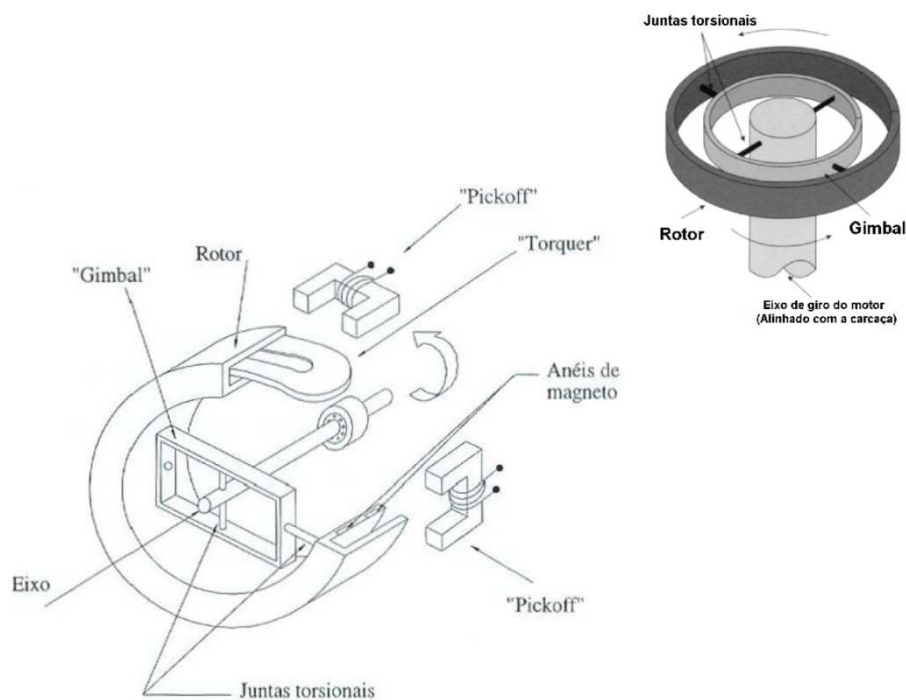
Representações do rotor e do eixo do motor de um Giro DTG
